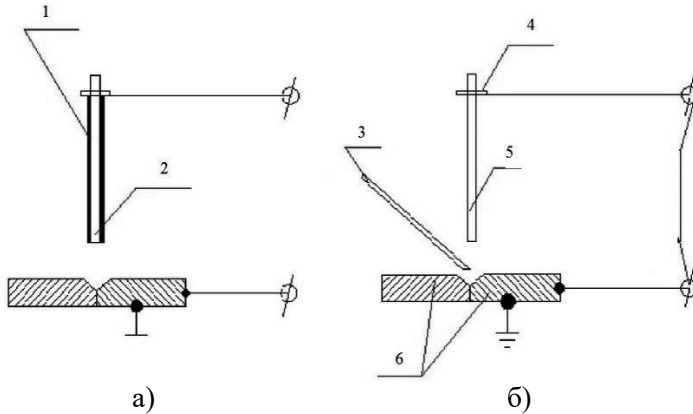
Схема дугового зварювання плавким (а) і неплавким (б) електродами: 1 – електродне покриття; 2 – плавкий електрод; 3 – присадний матеріал; 4 – електродотримач; 5 – неплавкий електрод; 6 – зварювальні частини виробу
